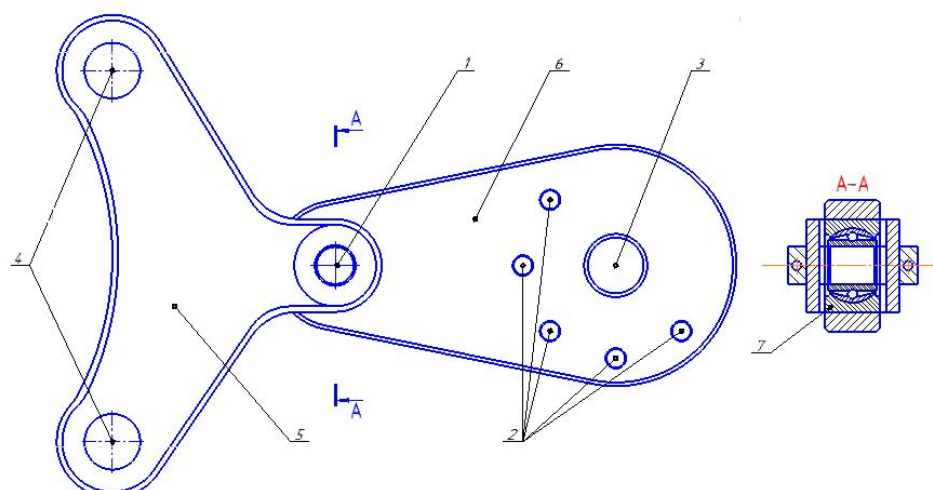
Шарнирная опора: 1 – соединительная ось; 2 – отверстие под болты; 3 – отверстие под ось; 4 – отверстия для крепления на переходной рамке; 5 – кронштейн переходной рамки; 6 – корпус шарнира; 7 – шарнир сферический подшипниковый
